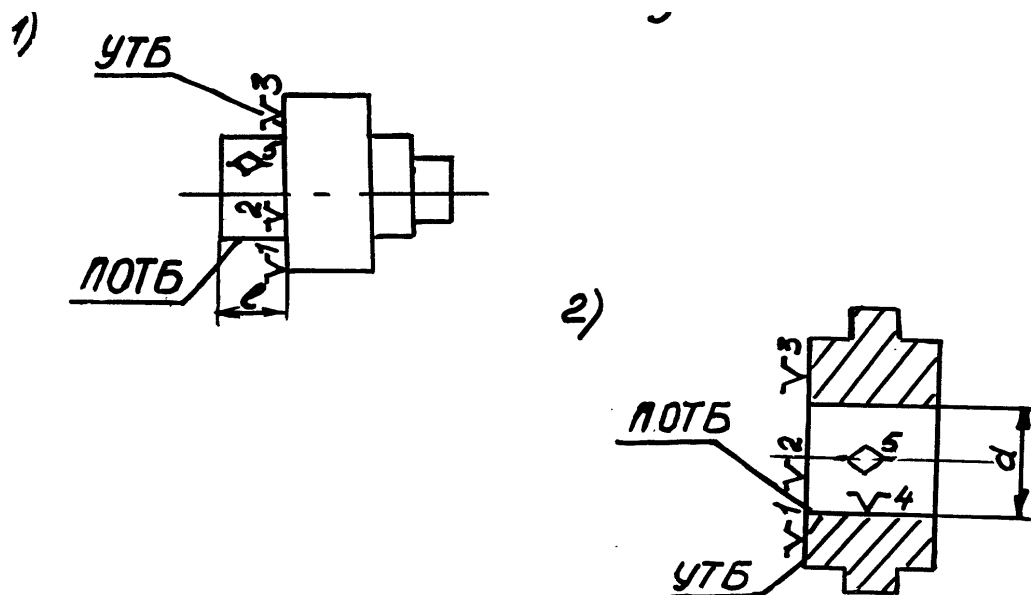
Теоретичні схеми базування коротких деталей типу тіл обертання
